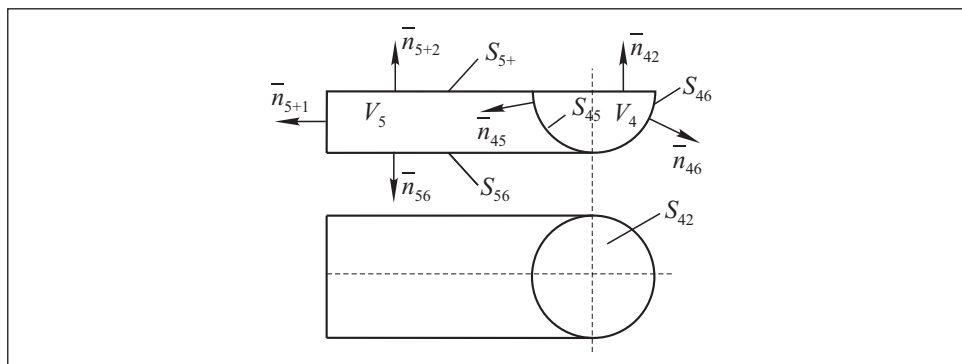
Схема ванны с расплавом полусферической формы и со сварным швом полуцилиндрической формы
